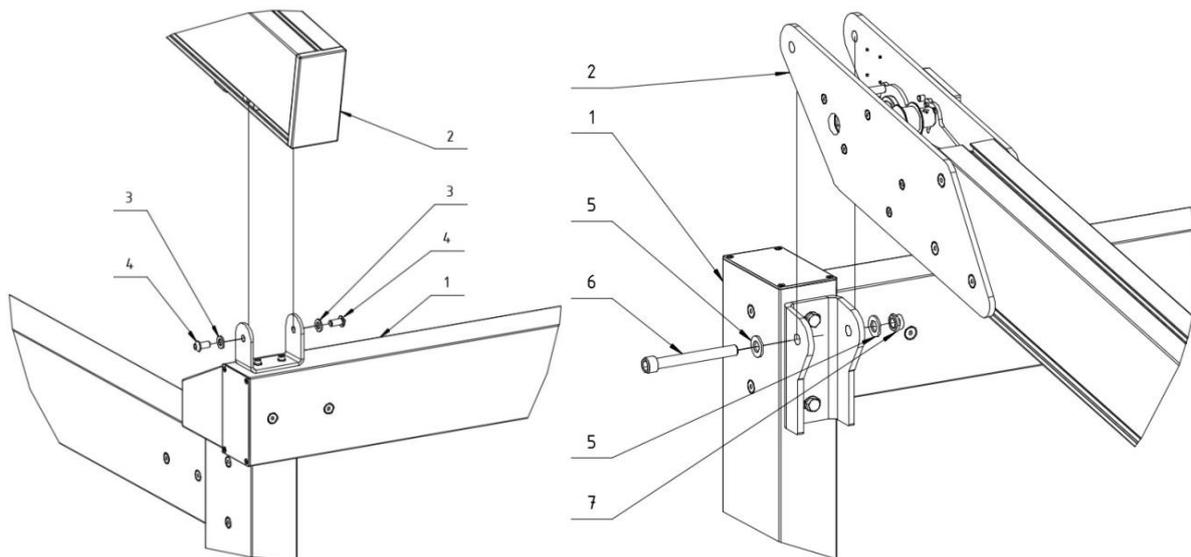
Manière de montage de la poutre de guidage : 1 – Construction porteuse, 2 – Poutre de guidage, 3 - Rondelle  $\varnothing 10,5$ , 4 - Vis M10x20, 5 - Rondelle  $\varnothing 15$ , 6 - Vis M14x120, 7 - Boulon M14.
